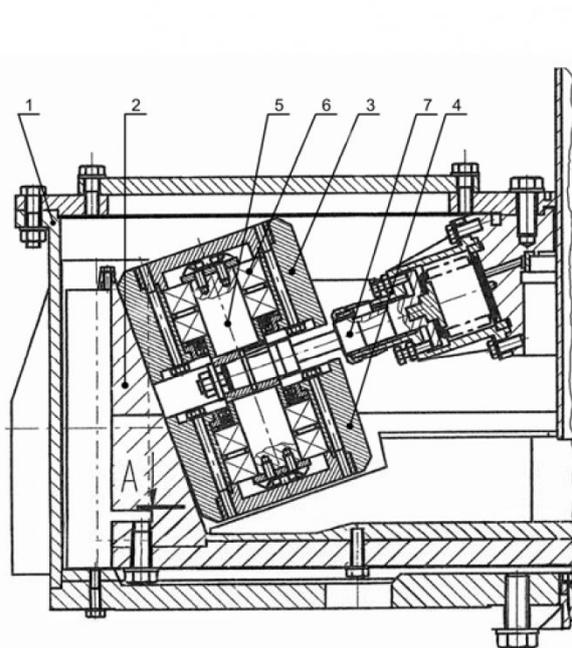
1- корпус мельницы; 2- обечайка; 3,4 – ролики; 5 - ось; 6 - подшипник; 7 - шток
